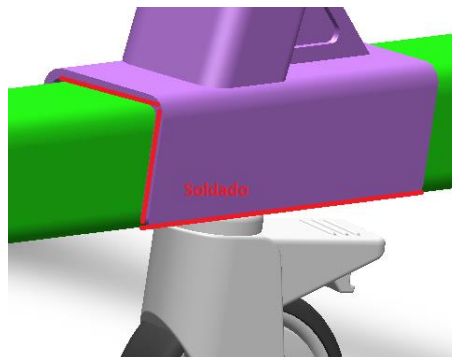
Vista de soldado de pieza N°3 para conforma la pata (Fuente 87)
